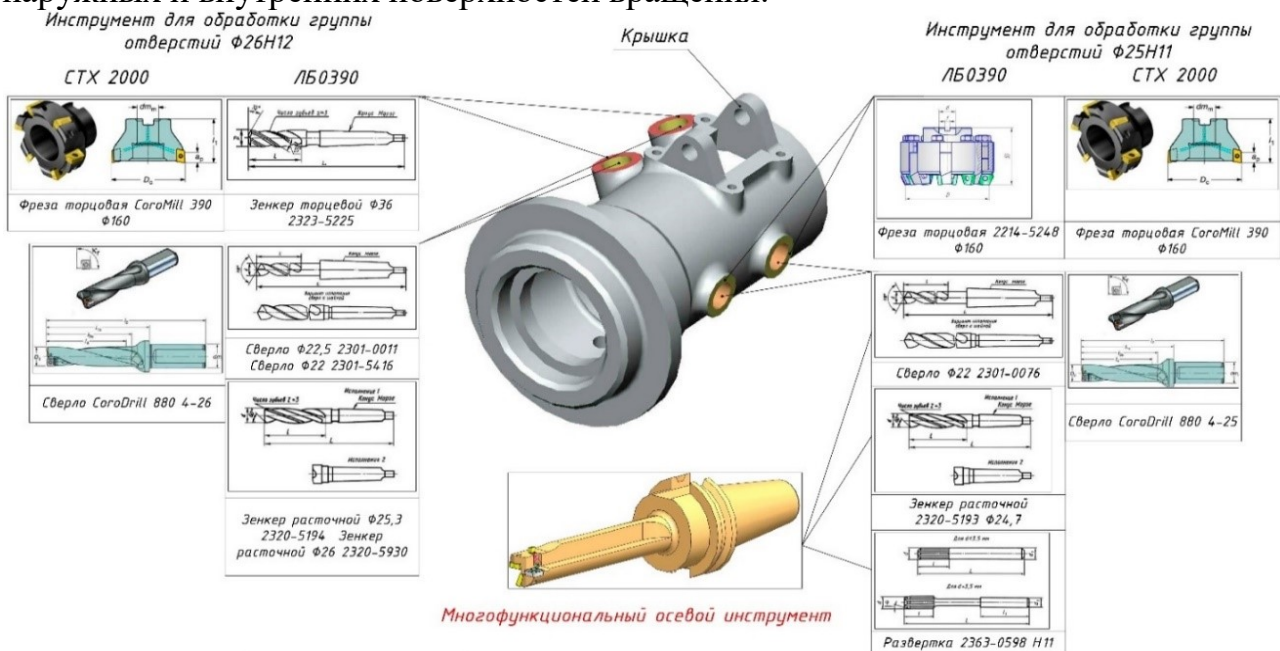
Обработка отверстий и бобышек в детали «Крышка»
